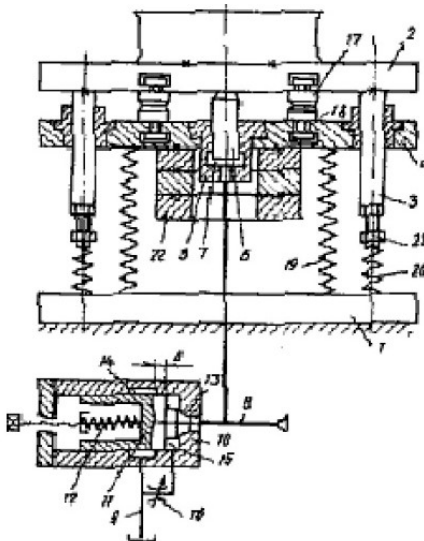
Конструктивна схема пристрою для вибивання ливарних форм
